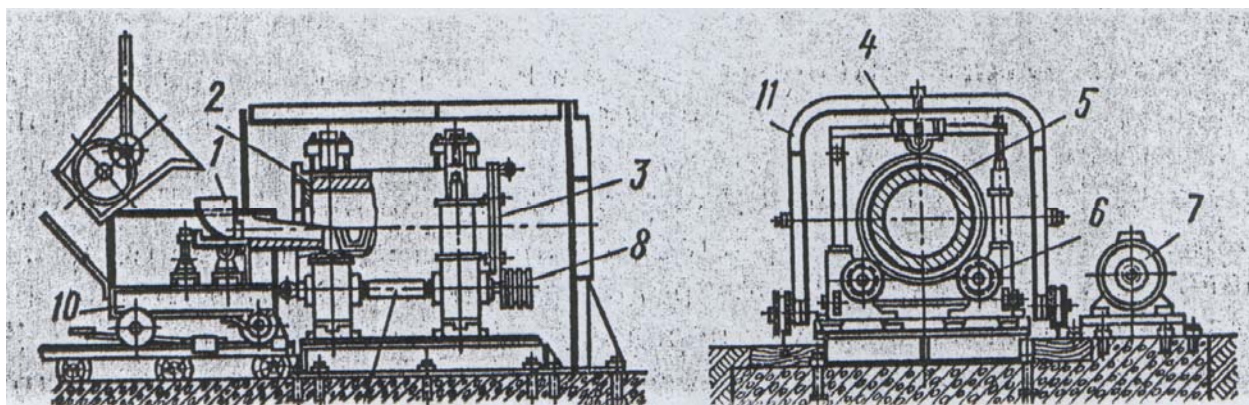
15. Роликовая центробежная машина. 1- желоб, 2- передняя крышка, 3- задняя крышка, 4- прижимные ролики, 5- форма, 6- опорные ролики, 7- электродвигатель, 8- клиноременная передача, 9- приводной вал, 10- тележка, 11- защитный кожух.
